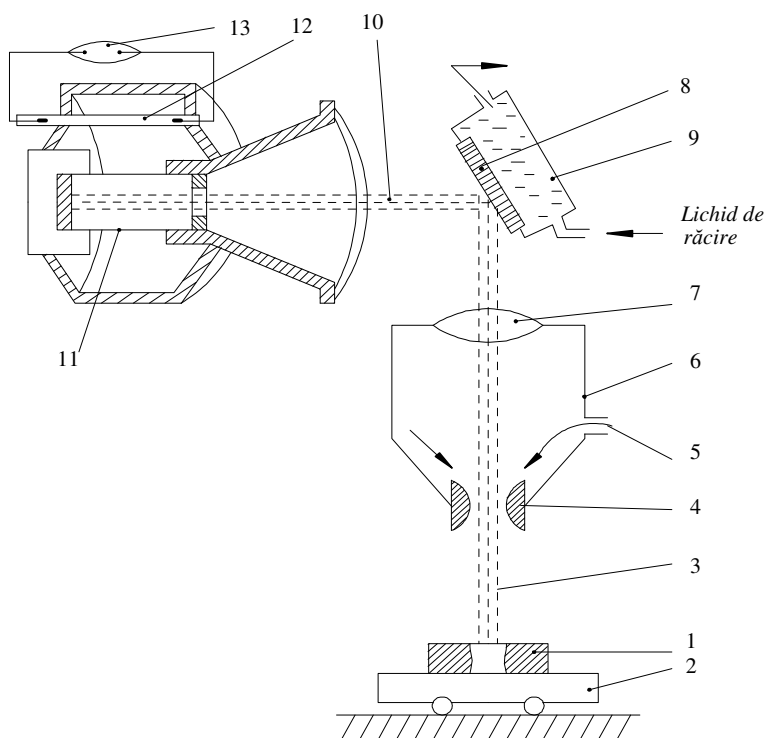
Schema de principiu a unei instalații de prelucrare dimensională cu fascicul laser cu mediu activ solid:
